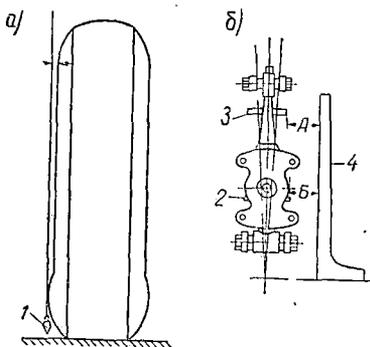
Проверка развала колес (а) и угла продольного наклона шкворня (б):
